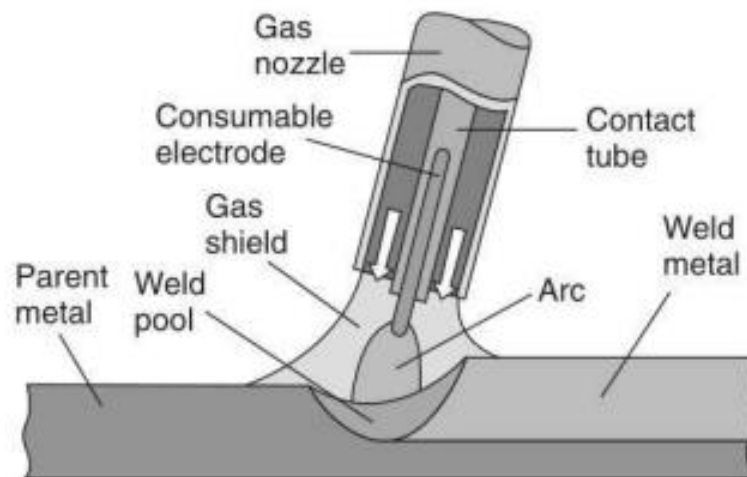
Representação esquemática da soldadura MIG [26]
